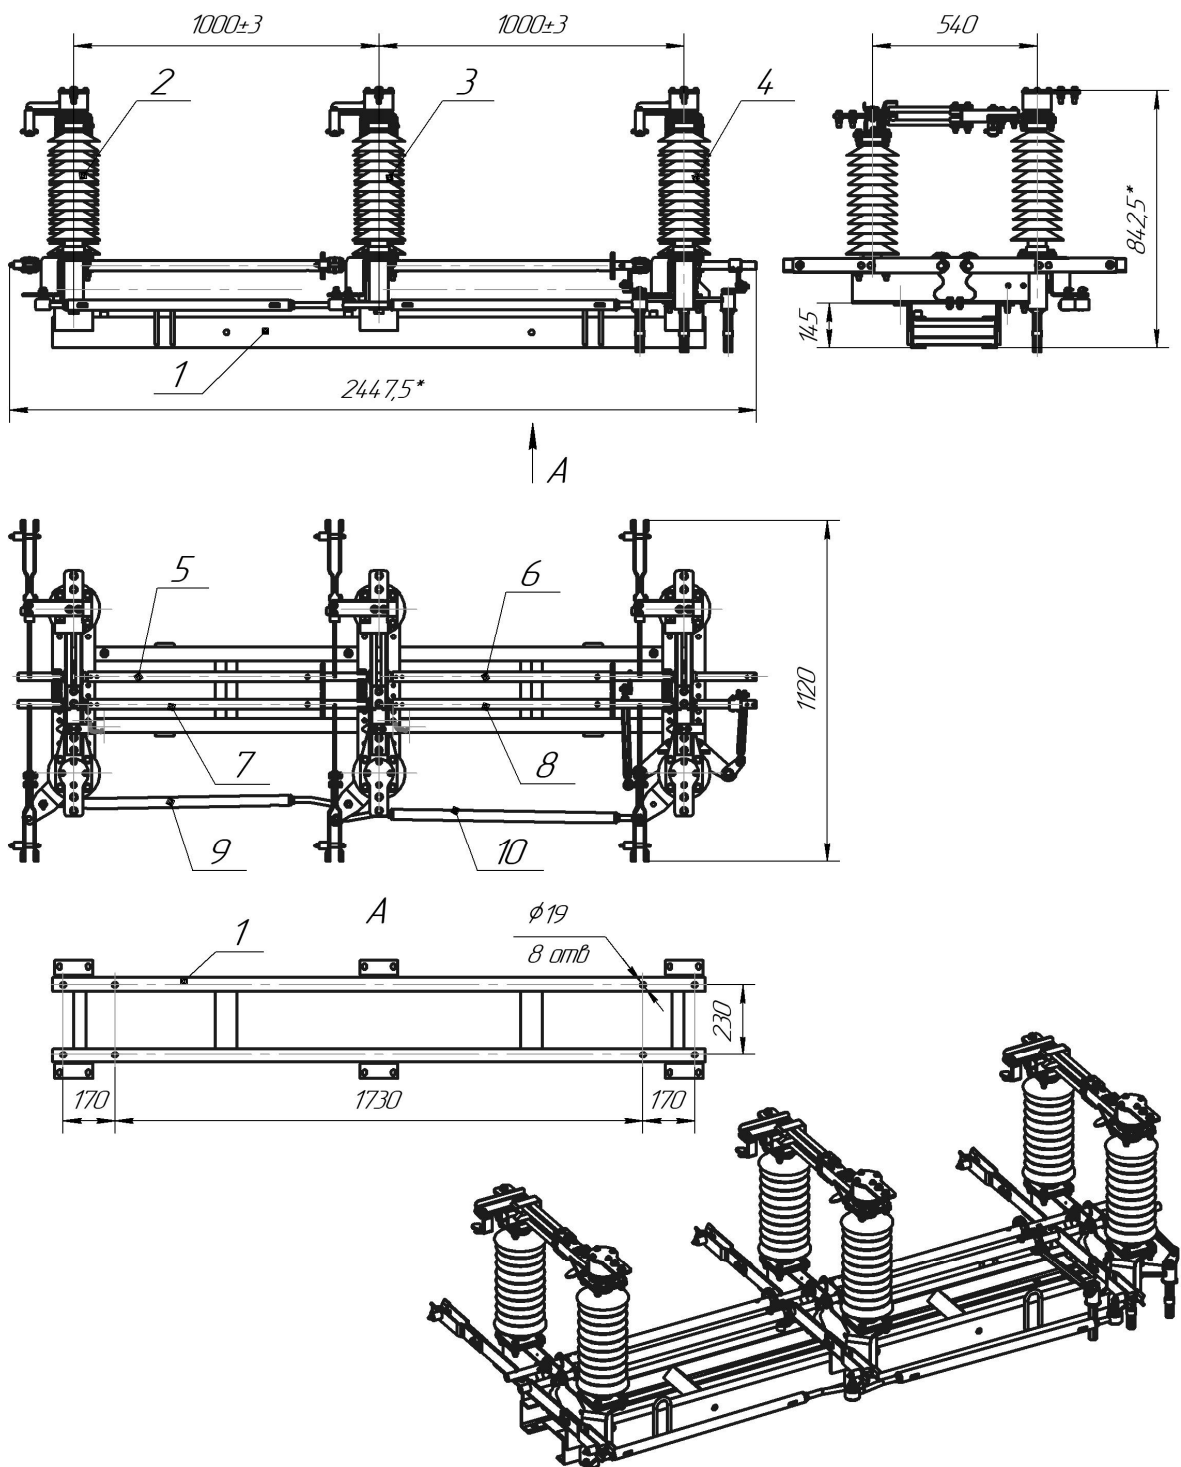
габаритные, установочные и присоединительные размеры базового исполнения трехфазного разъединителя РГП-НТ.2-35 / 1000 У1 с электродвигательными приводами главных ножей и заземляющих ножей
